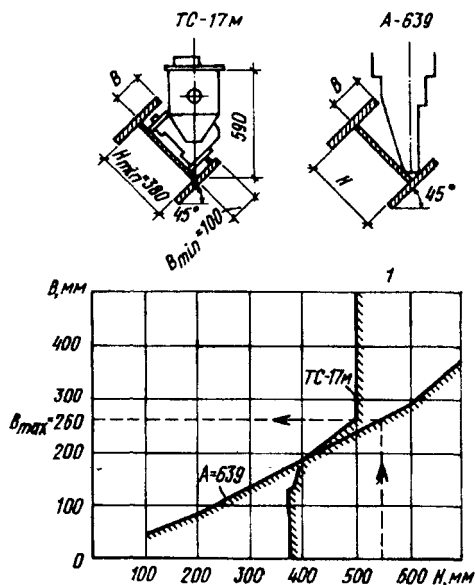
Предельные размеры сварного элемента при сварке трактором ТС-17 м и сварочной головкой А-639
